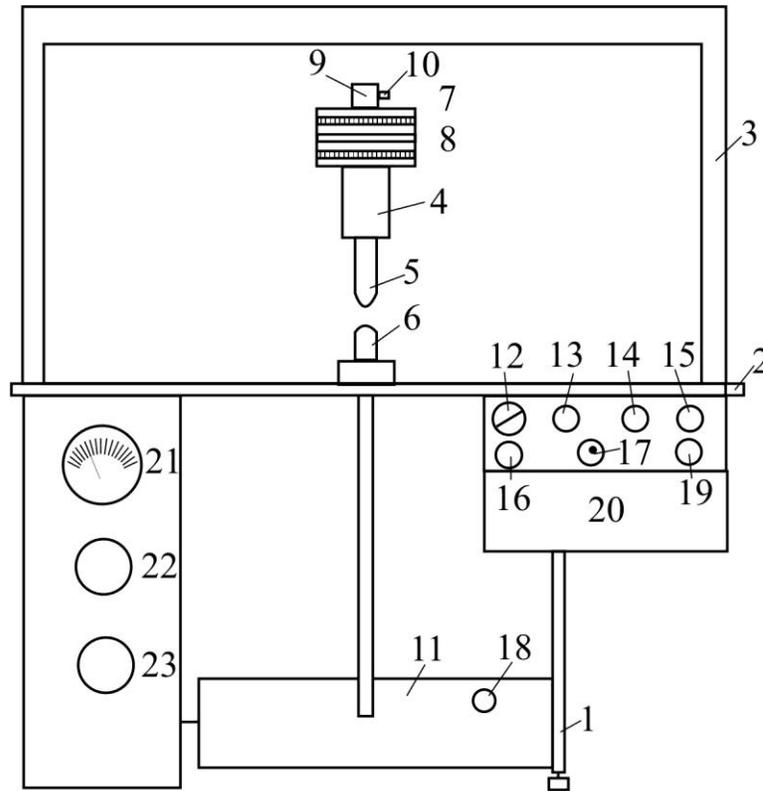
Установка точечной контактной сварки ССп-2:
